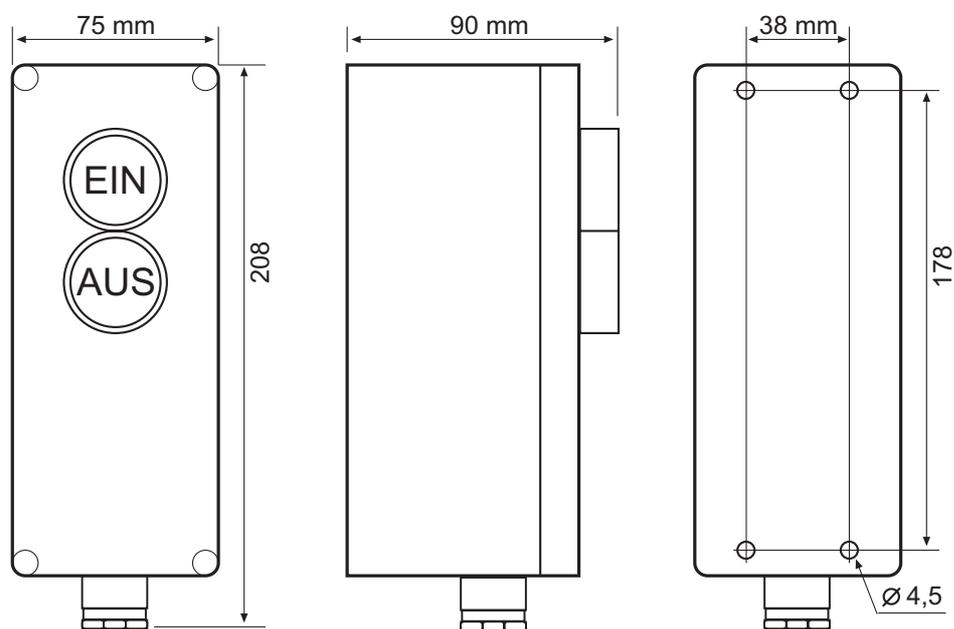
BG12-Ansichten; Front, Seite, Boden
